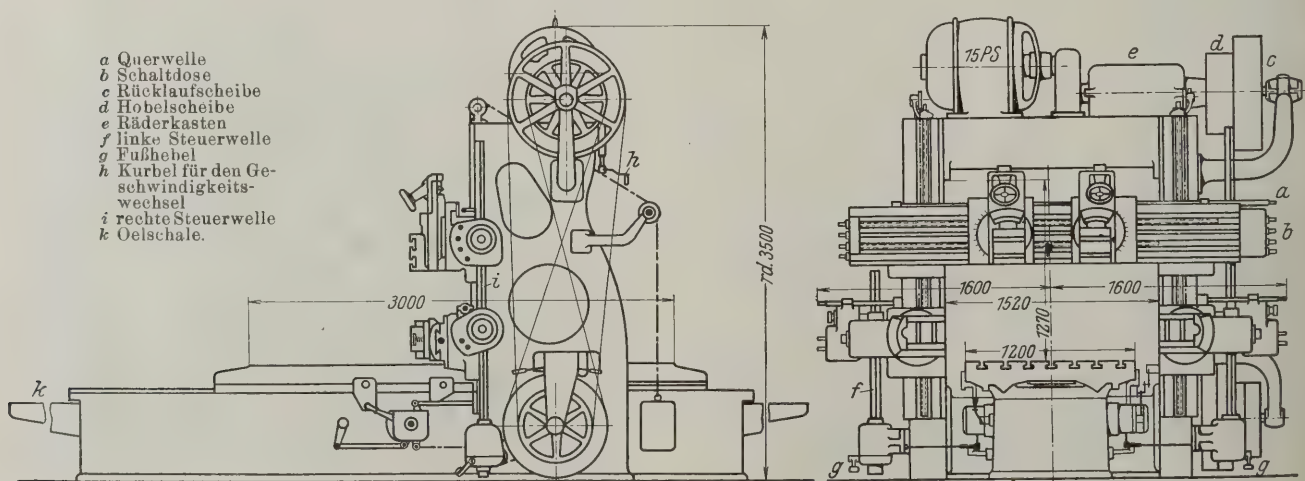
und 23. Tischhobelmaschine der Ernst Krause & Co. A.-G., Werkzeug-Masch.-Fabrik „Brunwerk“. 1500 mm Hobelbreite, 1250 mm Hobelhöhe.
